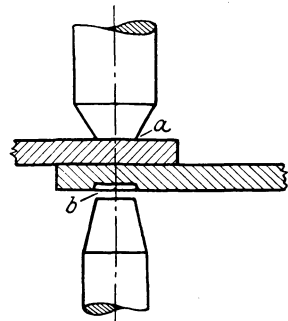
Elektroden für einseitige Schweißindrücke.
